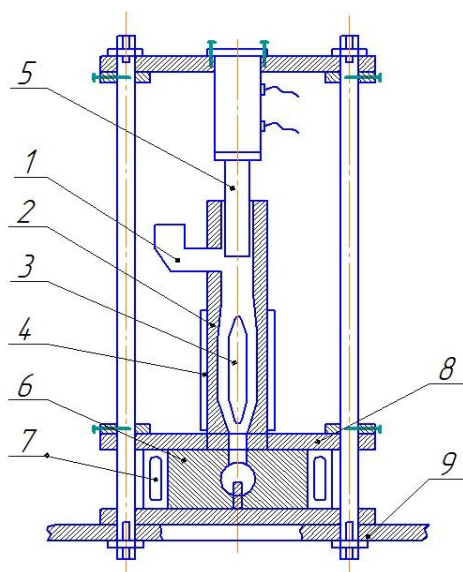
Схема установки для литья пластмассы под давлением [1]:
